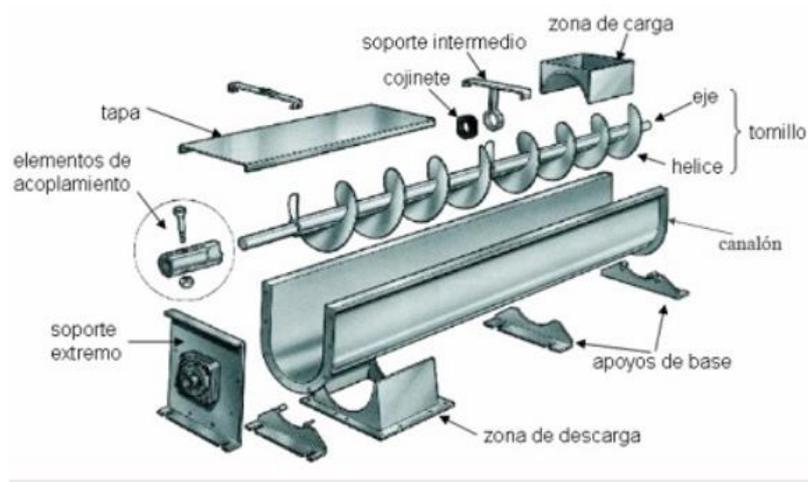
Despiece completo de un alimentador de tornillo sin fin
